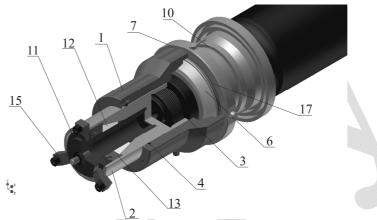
3D-модель конструкции устройства для гидрораспрессовки соединений с натягом колец подшипников с шейкой оси колесной пары
